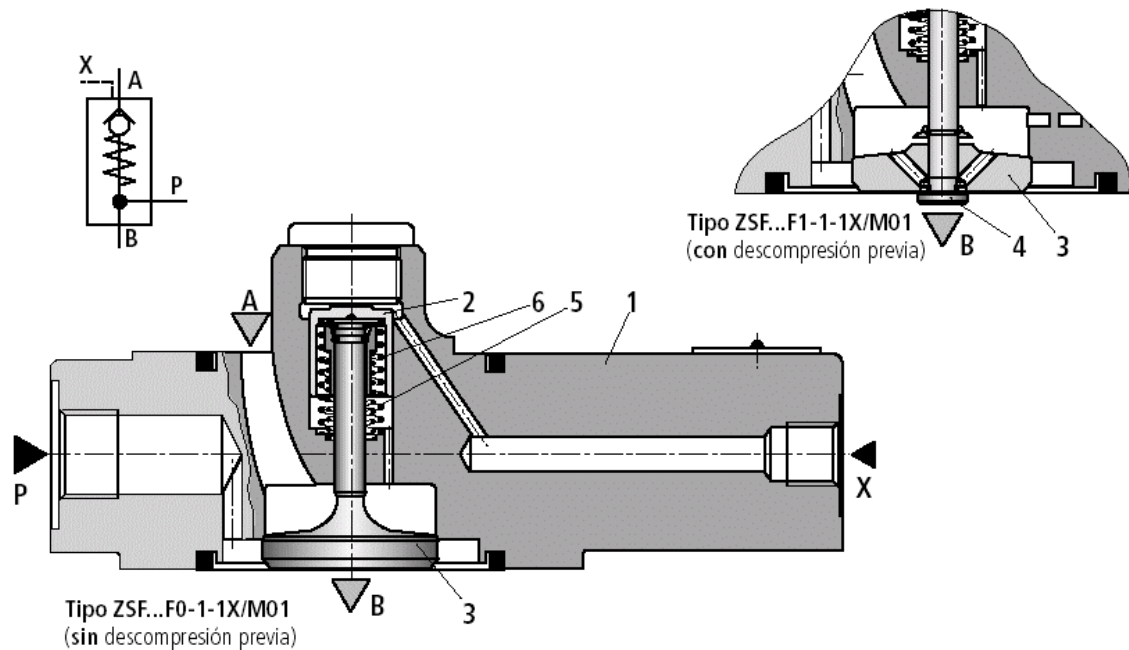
Válvula de prellenado de BOSCH-REXROTH.
